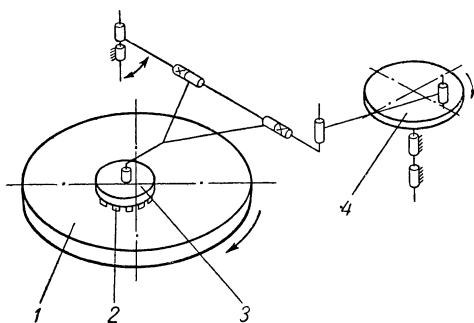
Схема станка для односторонней шлифовки с вращающимся шлифовальником и качающейся шайбой.
